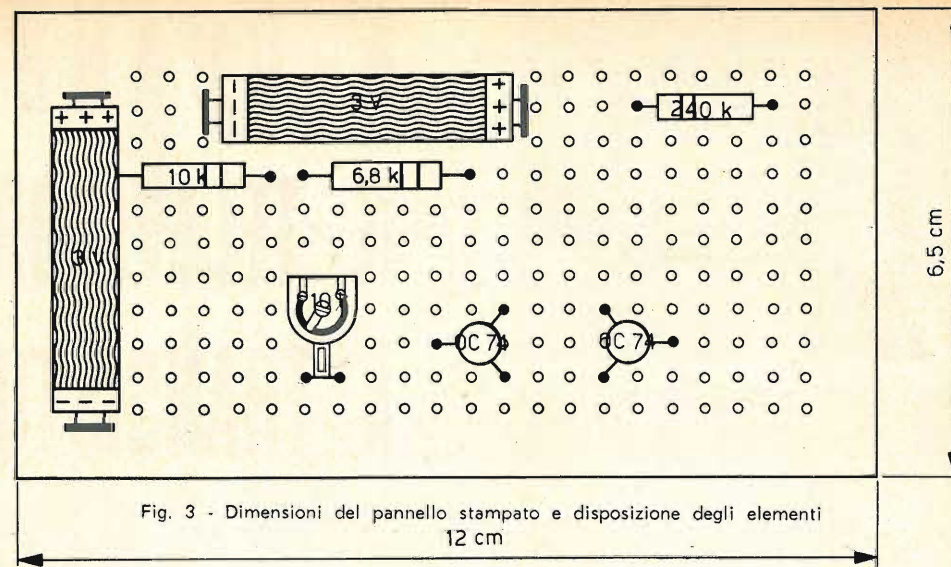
Dimensioni del pannello stampato e disposizione degli elementi
